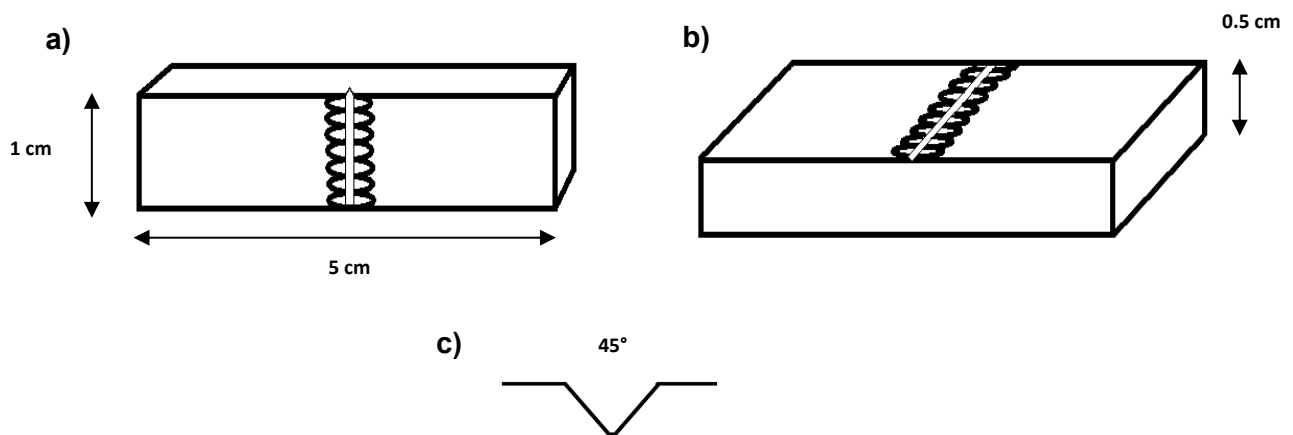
Dimensiones utilizadas en las probetas de impacto para ensayo Charpy.
